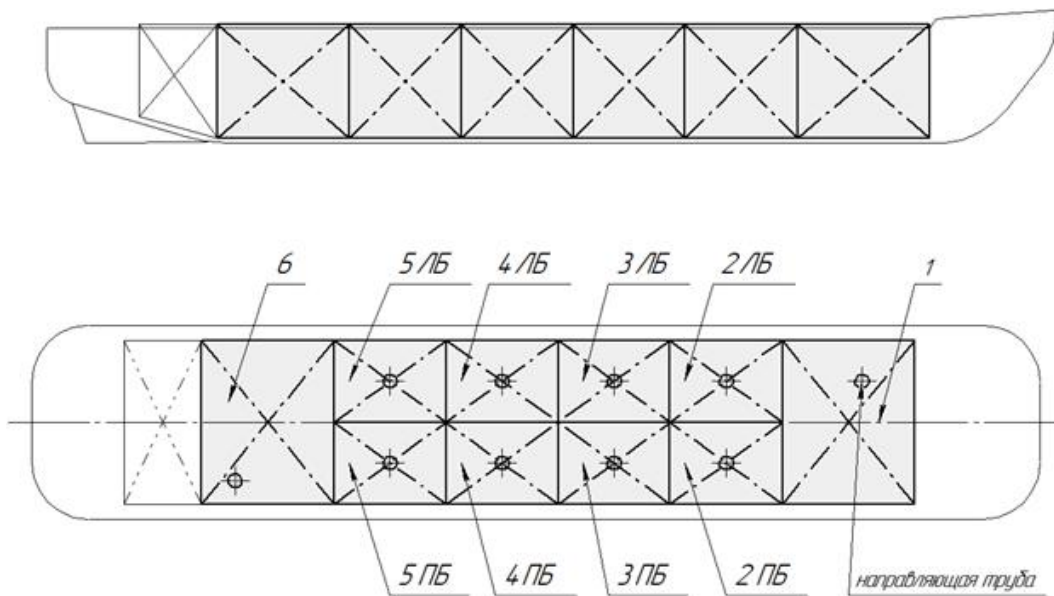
Эскиз общего вида и расположение резервуаров РГС-550, РГС-420, РГС-520
